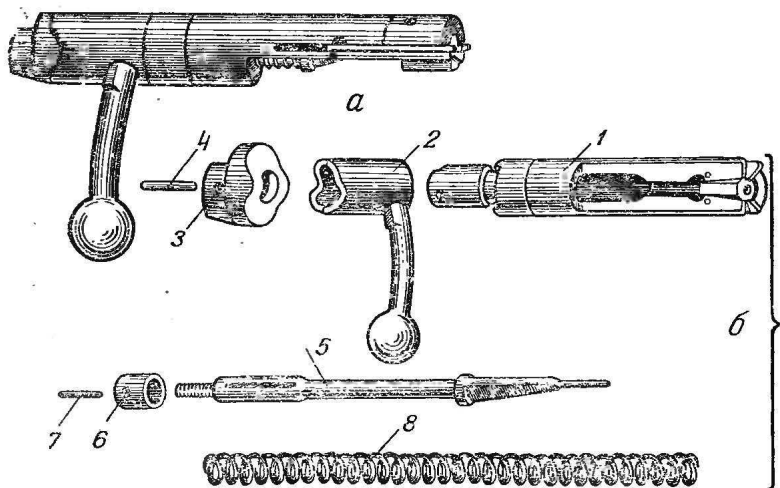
Затвор: а — в собранном виде; б — детали затвора; 1 — боевая личинка; 2 — стебель затвора с рукояткой; 3 — курок; 4 — шпилька курка; 5 — ударник; 6 — муфта; 7 — шпилька муфты; 8 — боевая пружина
